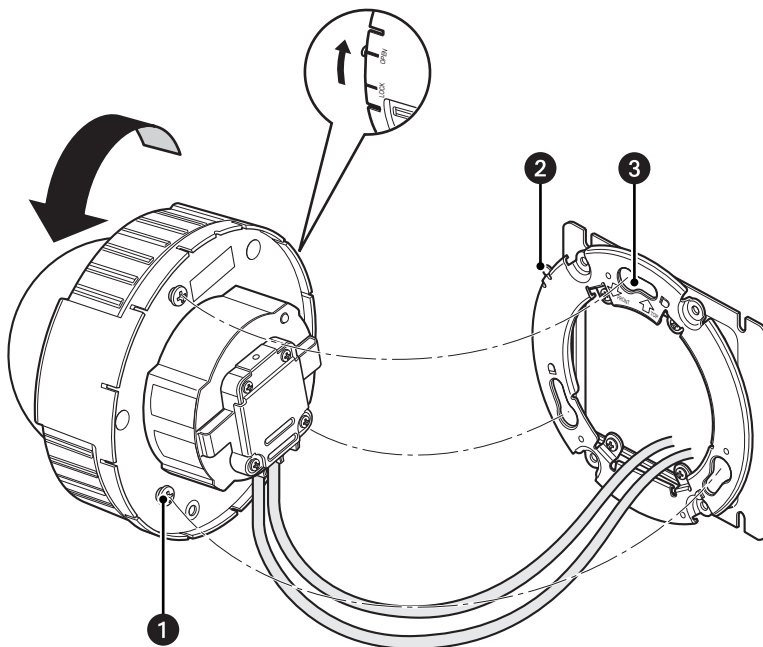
Установка камеры на сдвоенную клеммную коробку
